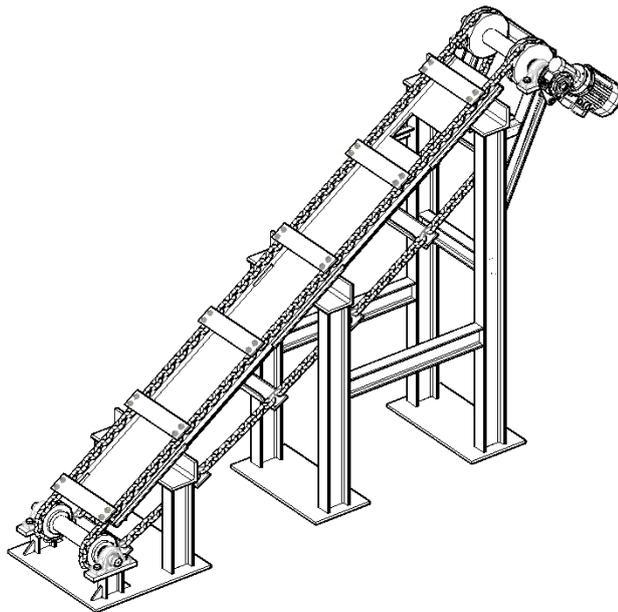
Elevador representado en AutoCAD. Fuente: elaboración propia.
